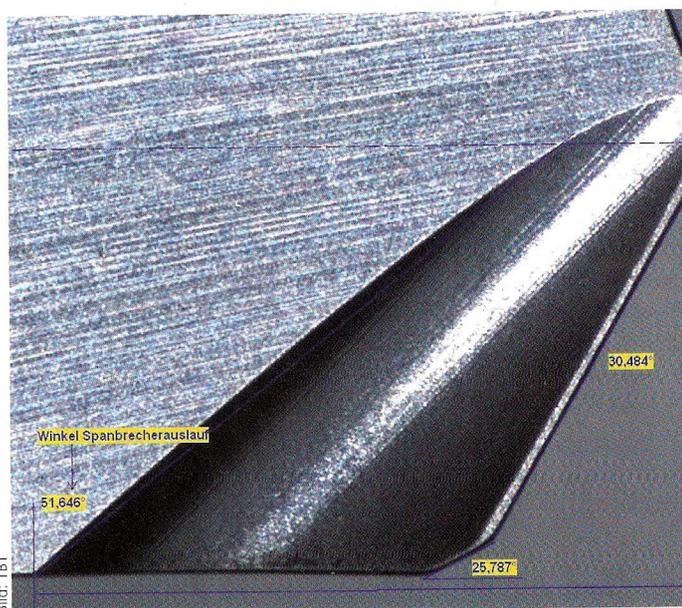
Detailaufnahme der Schneidengeometrie mit speziellem Spanformer.
